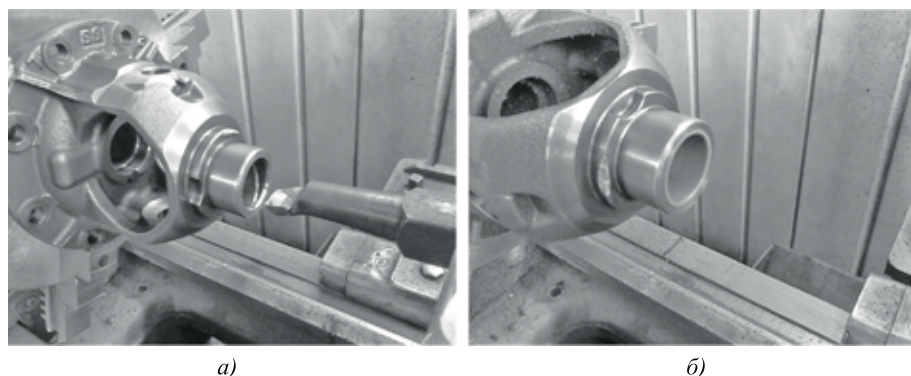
Процесс ремонта чашки дифференциала: а — расточка; б — установка втулки из материала МАС
